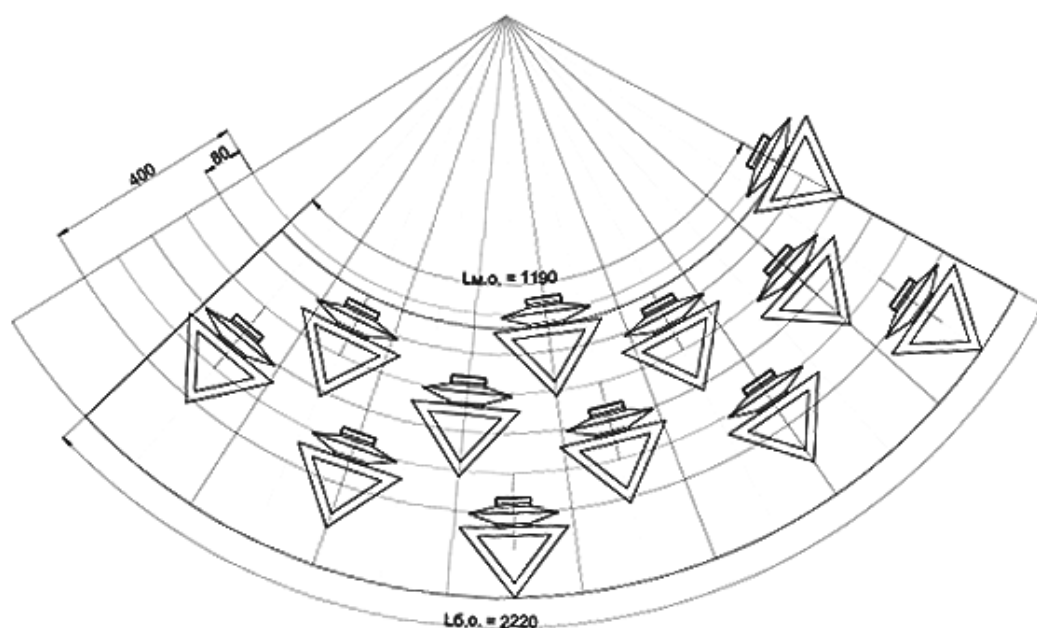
Развертка схемы набора дискового инструмента на радиальной реверсивной коронке
